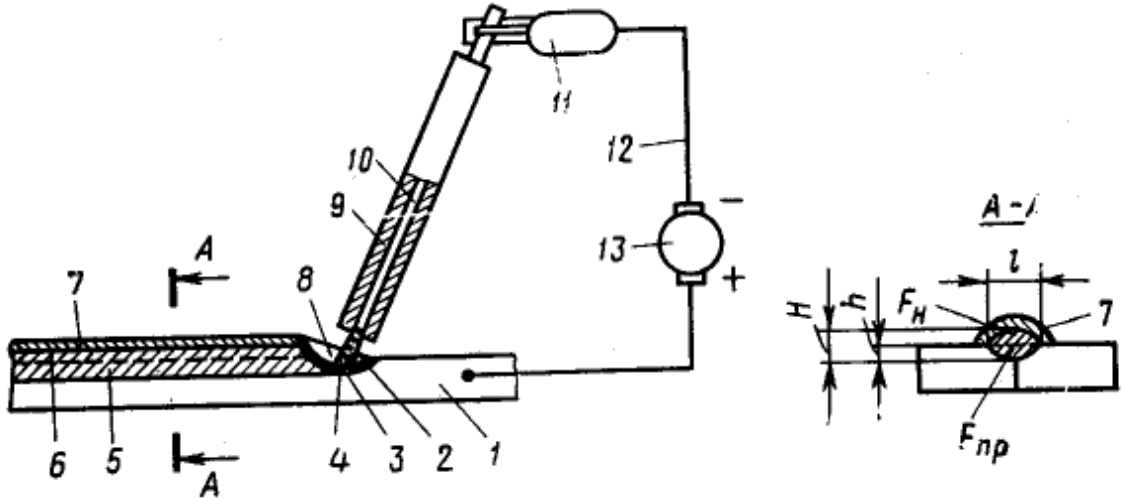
Схема ручной дуговой сварки:
